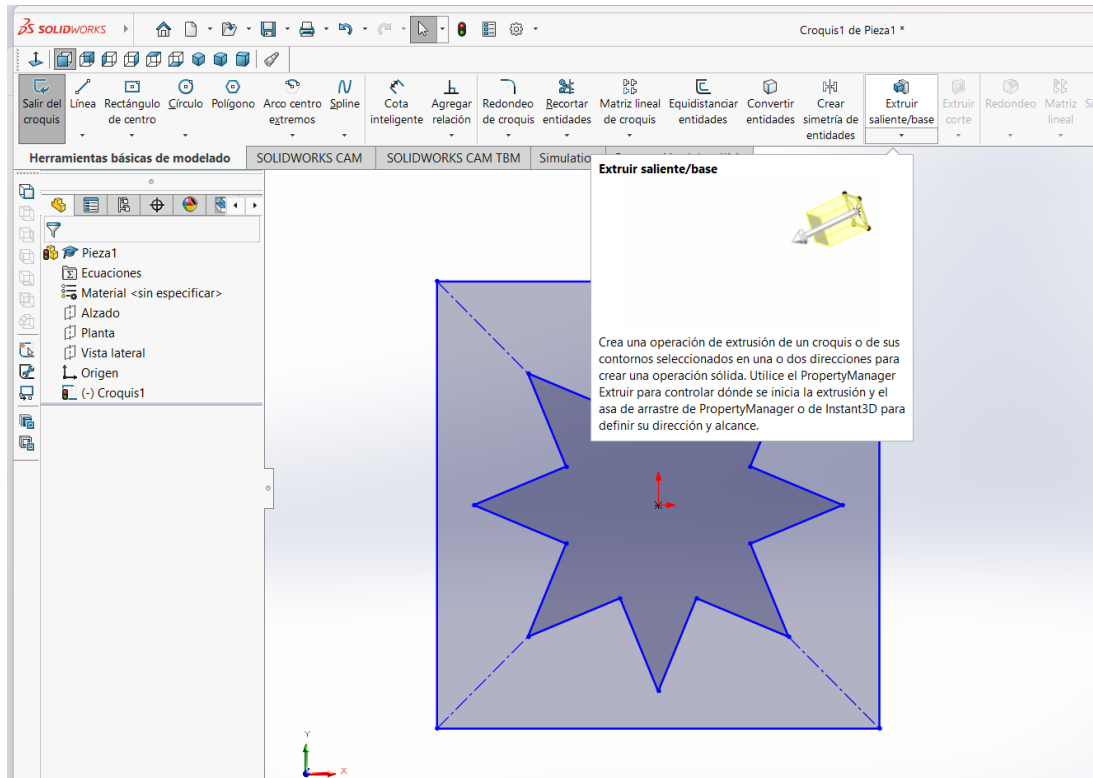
Extrusión 1 Corte avanzado. Fuente: Creación propia
